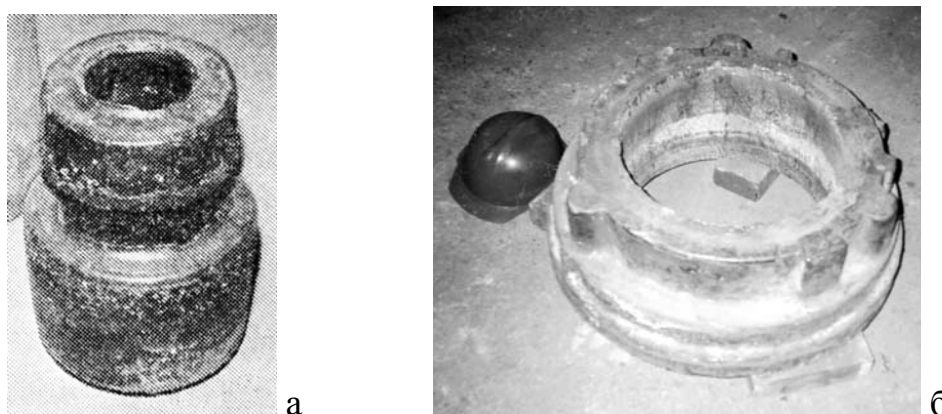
Внешний вид отливок ЦЭШЛ для двух внешних зубчатых венцов шестерни из стали 20X2H4A (а) и для одного внутреннего зубчатого венца в корпусе редуктора из стали 40 Л (б).
